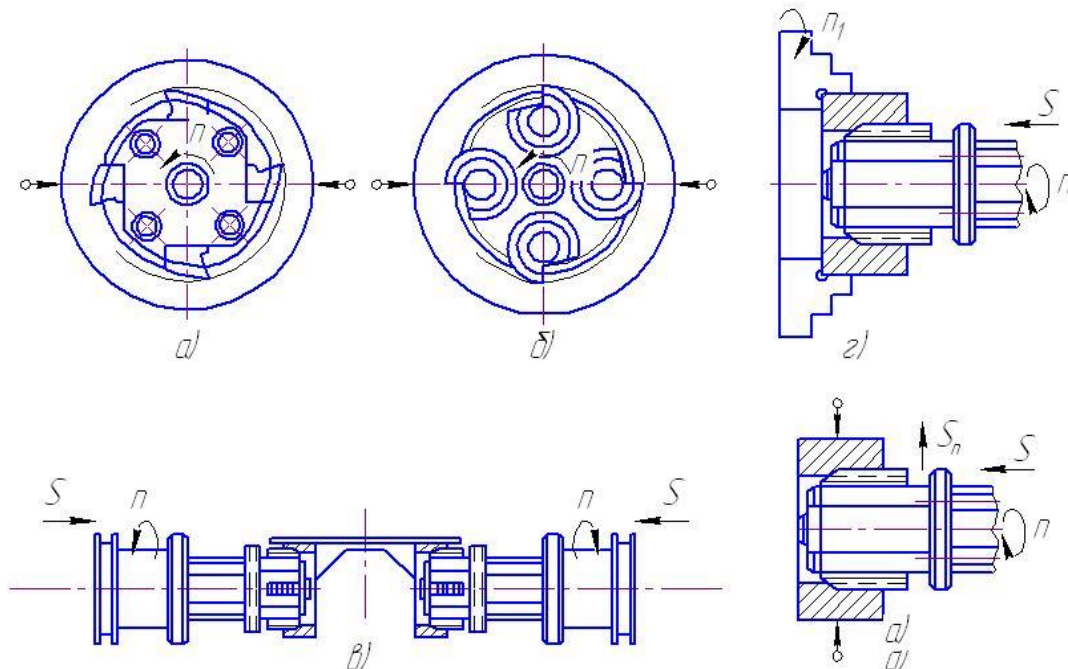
Нарезание резьбы головками: а) с призматическими гребенками; б) с круглыми гребенками; в) одновременная обработка двух резьб; г) работа при одновременном вращении инструмента и заготовки; д) многопроходное нарезание резьбы
